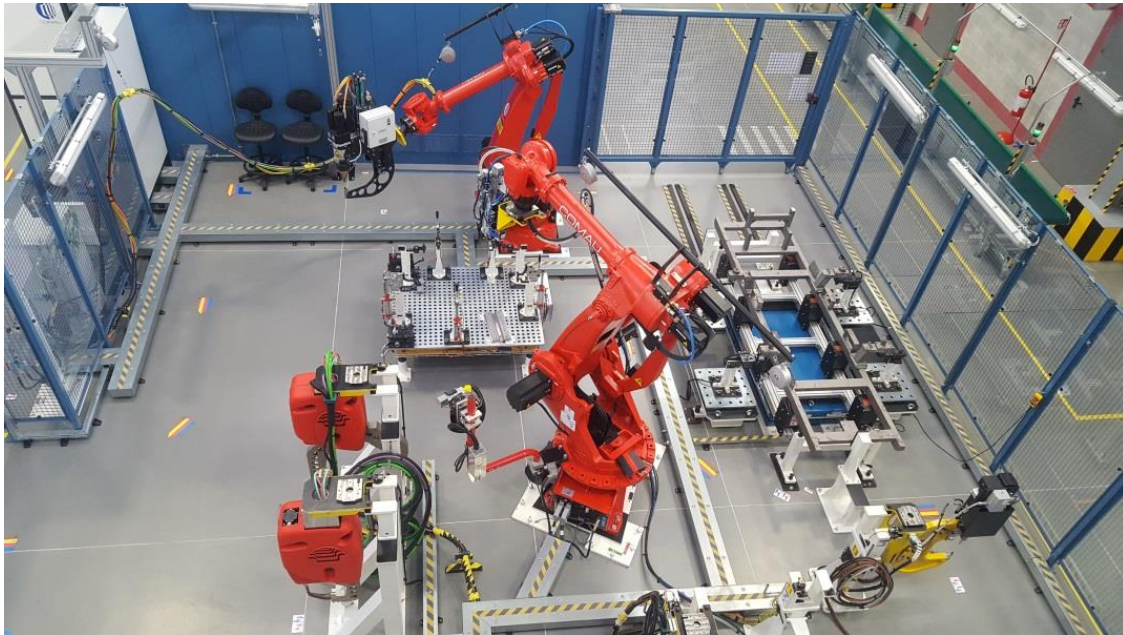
Sistemi robotizzati di saldatura che simulano i sistemi in produzione degli stabilimenti FCA: processi di saldatura “Cold Metal Arc Welding” (particolare processo GMAW); laser (Fibra/Diodo); resistenza RSW e Spot Friction Stir Welding SFSW.
